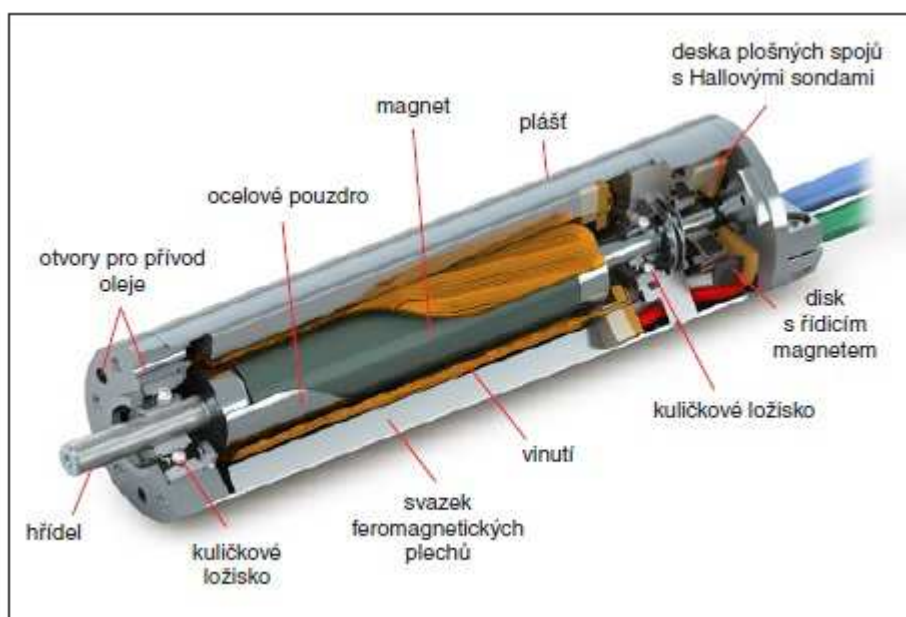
Uspořádání rotoru motoru EC 22 HD
